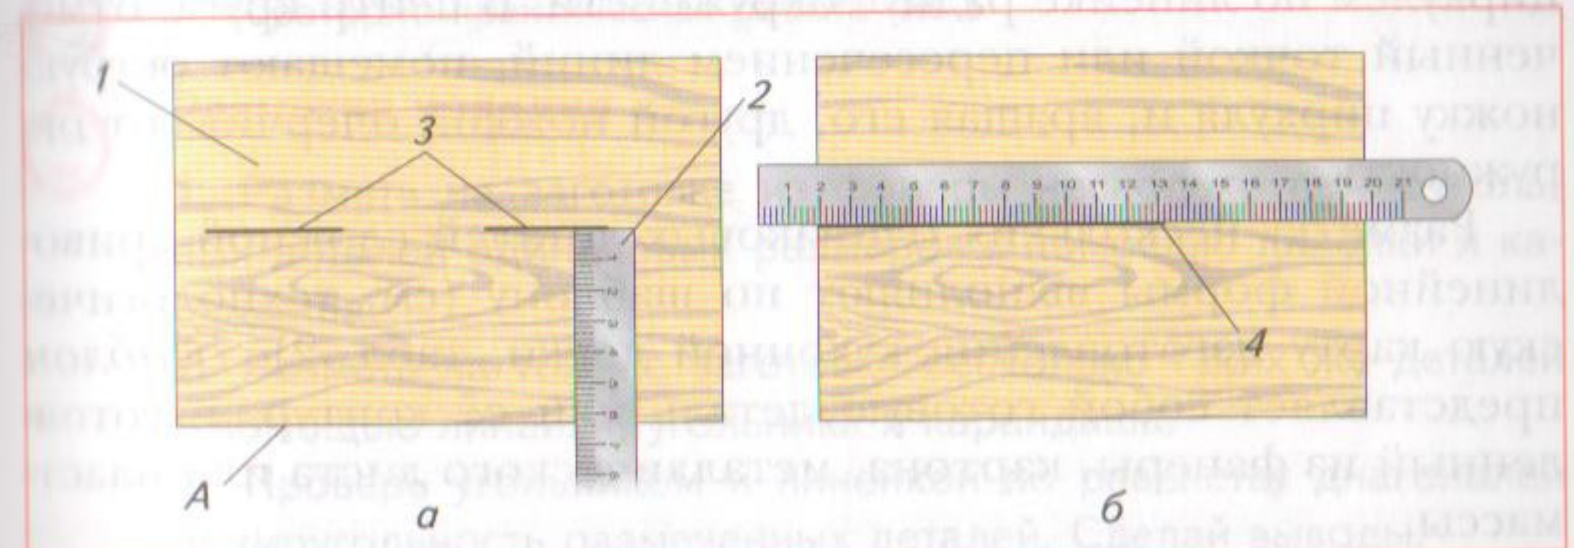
Разметка бруска по ширине линейкой: а — нанесение рисков ширины бруска; б — проведение разметочной линии; 1 — заготовка; 2 — линейка; 3 — риски; 4 — разметочная линия; А — базовая кромка
